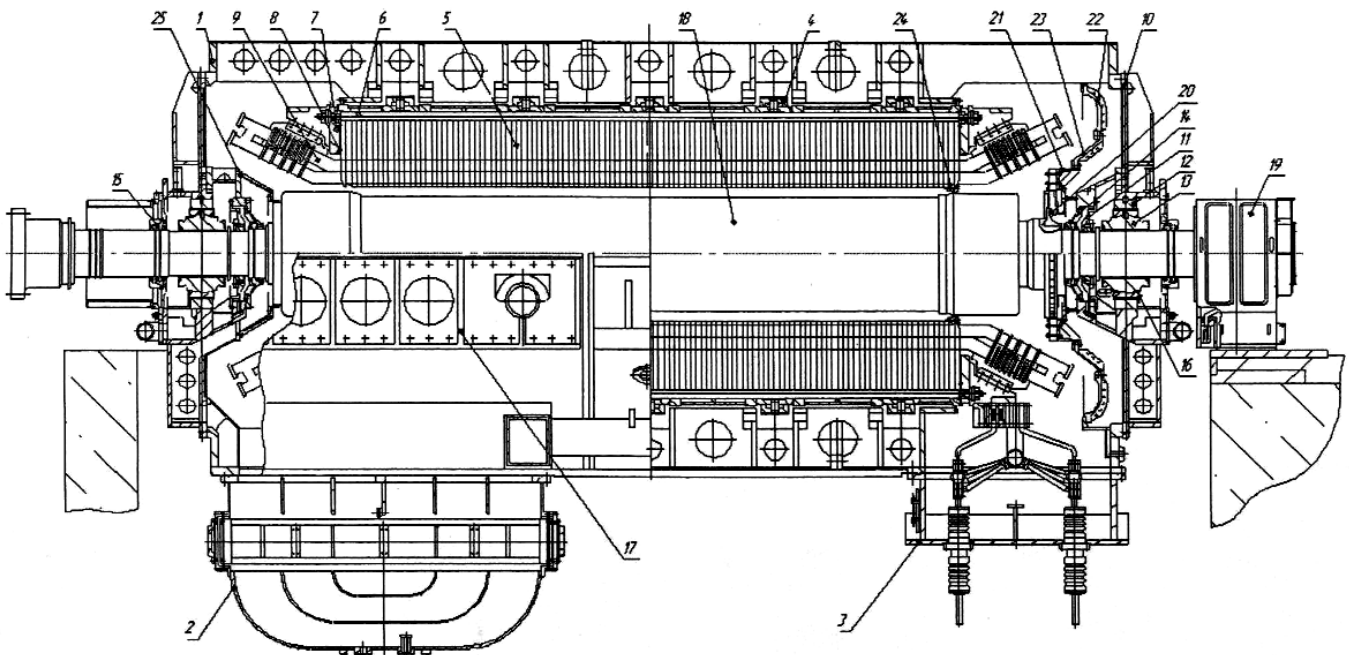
Продольный разрез турбогенератора ТГВ-300. 1 — корпус статора; 2 — коробка газоохладителей; 3 — коробка выводов; 4 — подвеска сердечника; 5 — сердечник статора; 6 — стяжная призма; 7 — фланец нажимной; 8 — медный экран; 9 — обмотка статора; 10 — щит наружный; 11 — уплотнение вала; 12 — обойма; 13 — вкладыш; 14 — маслоуловитель внутренний; 15 — маслоуловитель наружный; 16 — установка гидроподъема; 17 — лапа; 18 — ротор; 19 — аппарат щеткодержателей; 20 — компрессор; 21 — диффузор; 22 — щит внутренний; 23 — щит промежуточный; 24 — уплотнение воздушного зазора; 25 — кожух перепускной
